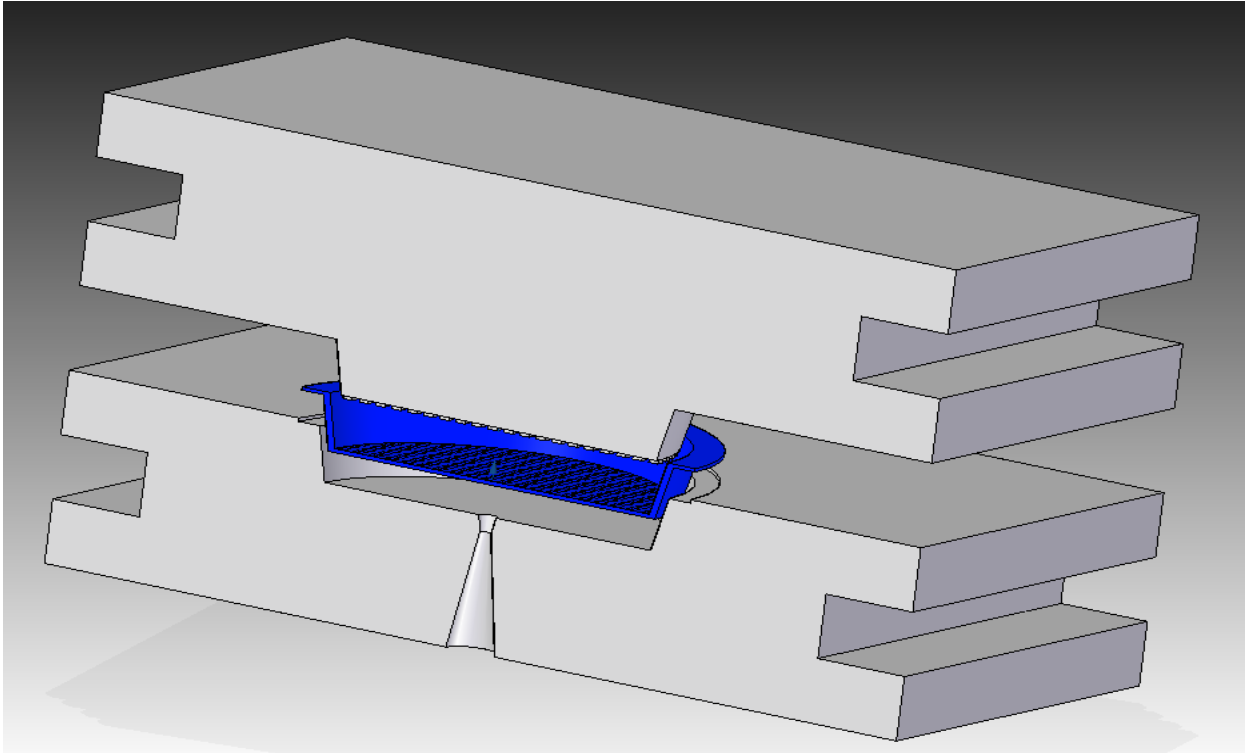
vista em corte e explodida do fechamento do molde, com a peneira inserida.
